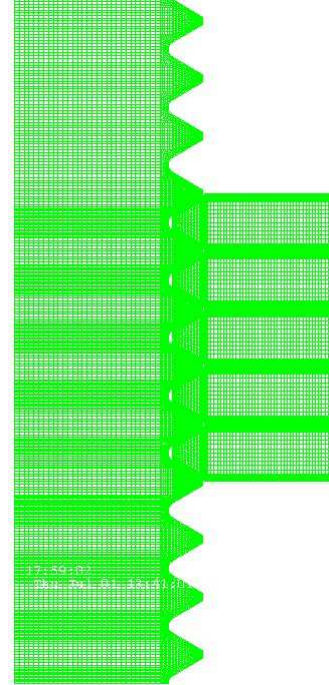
Vue d'ensemble du modèle éléments finis axisymétrique du boulon.
